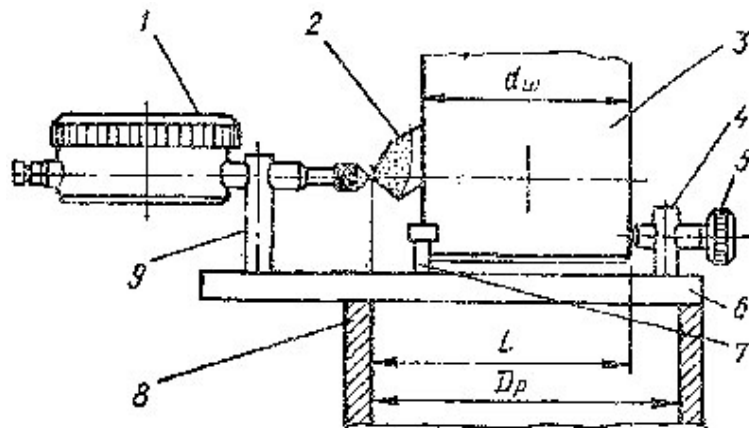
Індикаторний пристрій для встановлення вильоту різця:
